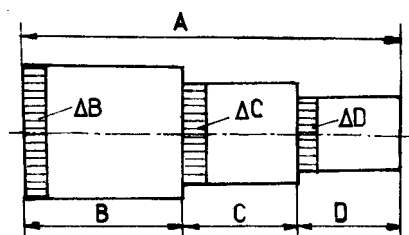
Schemă pentru determinarea abaterilor elementului de închidere
